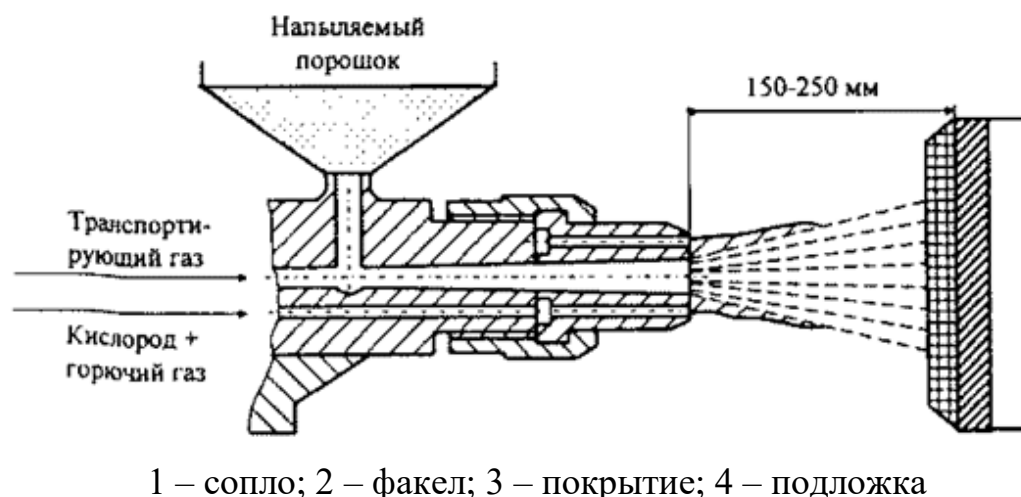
Схема газопламенного напыления порошкового материала с помощью транспортирующего газа
